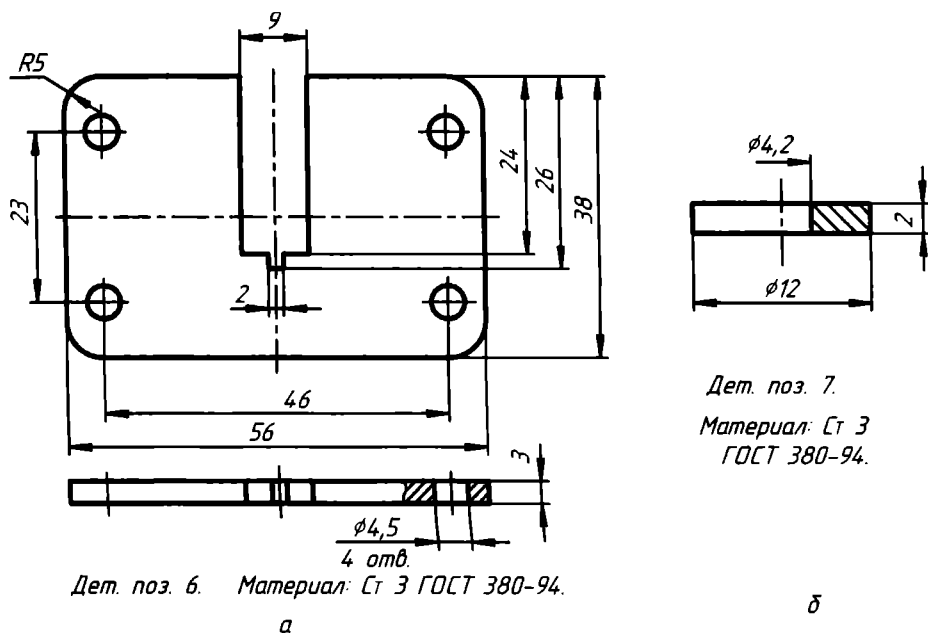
Чертежи: а — пластины; б — шайбы
